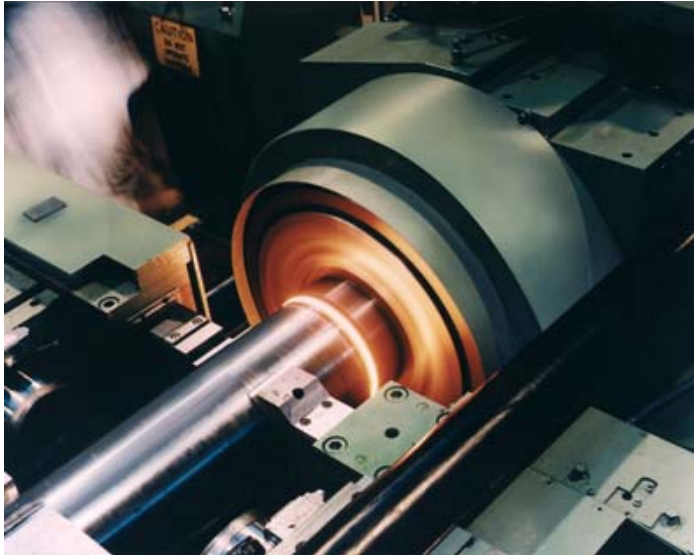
Ejecución de la soldadura por fricción radial. Fuente: Zimmer *et al.* (2010).
